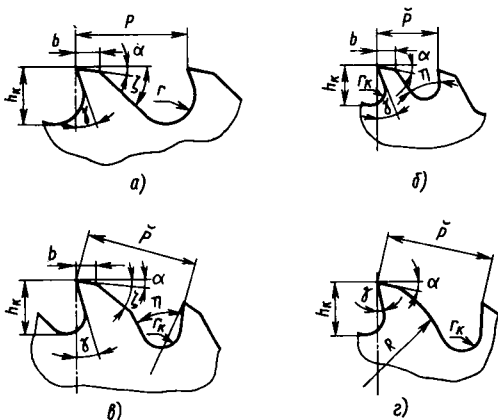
Типовые формы зубьев и впадин многозубых инструментов с главным движением:
